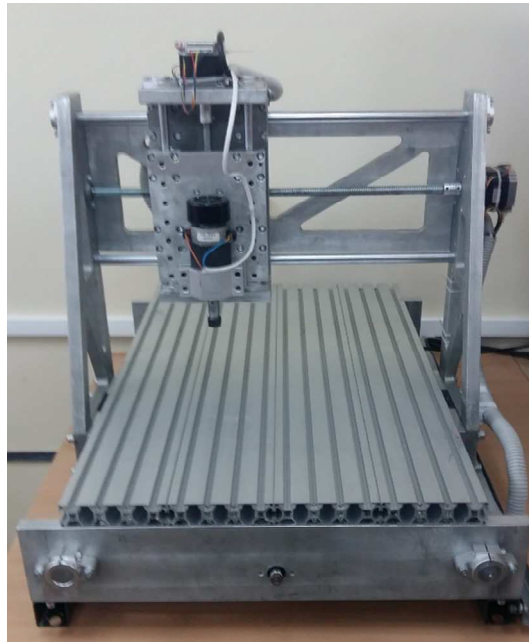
Трикоординатний фрезерний верстат з ЧПК моделі CN 2
